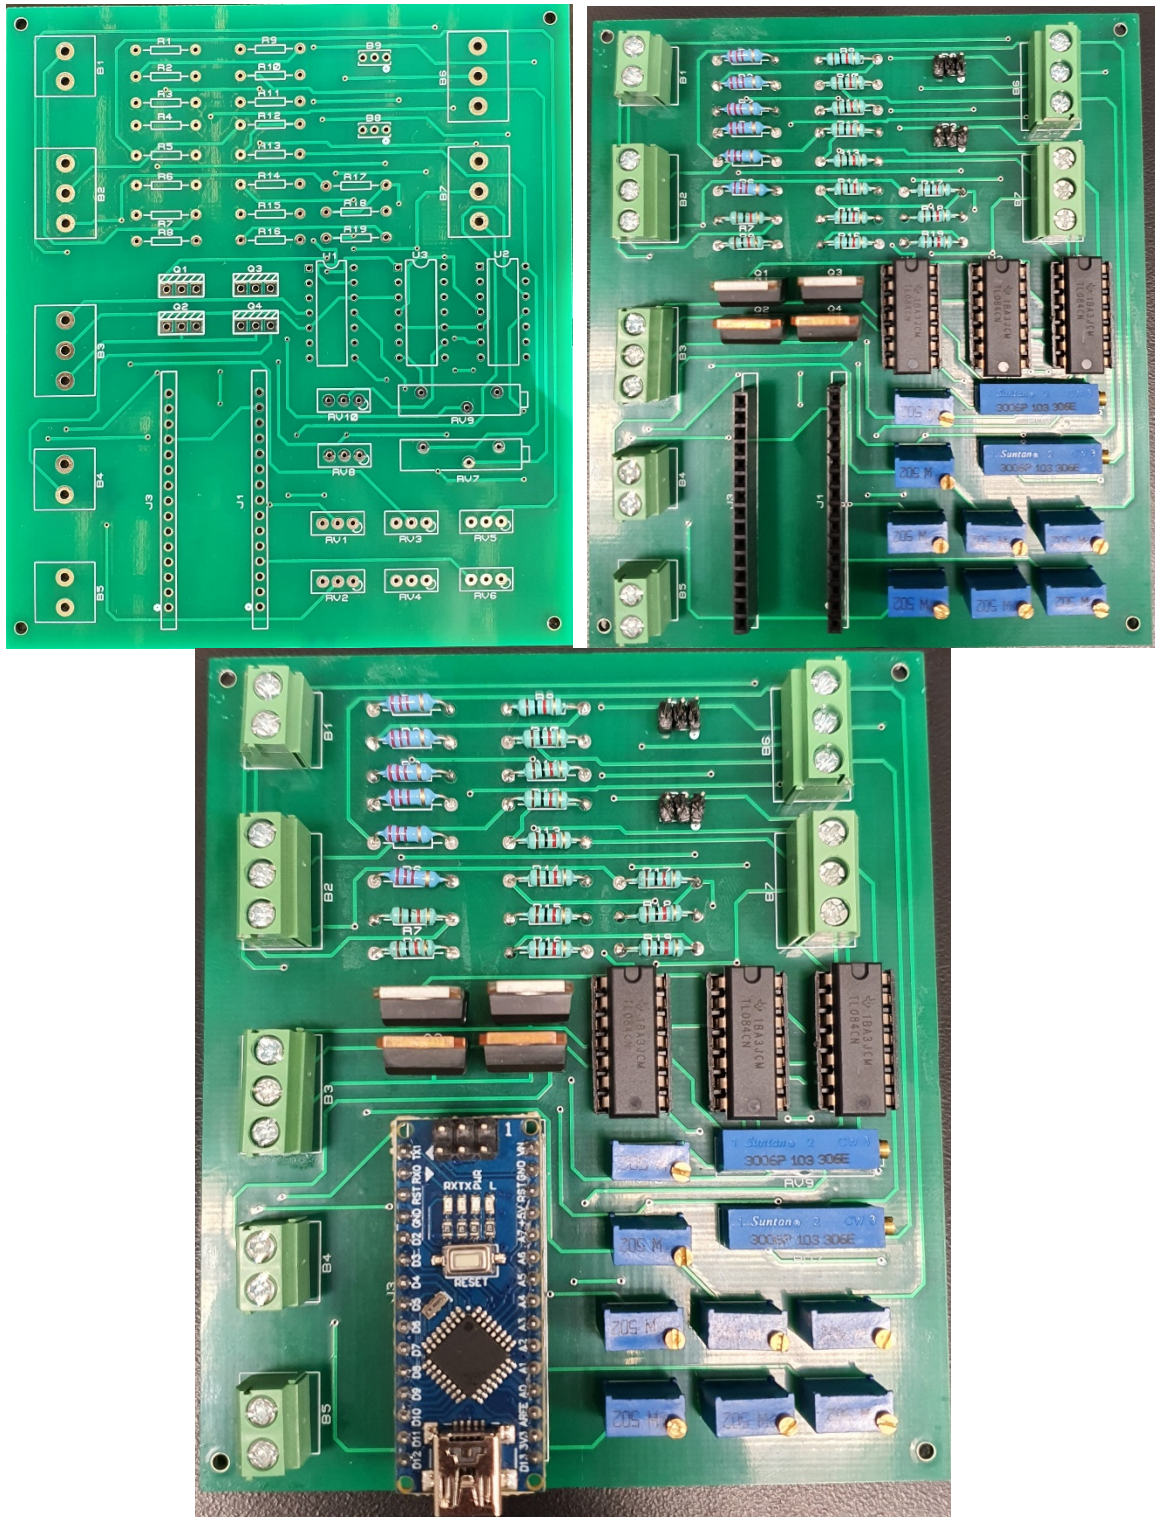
IMÁGENES DE PCB EN FÍSICO
